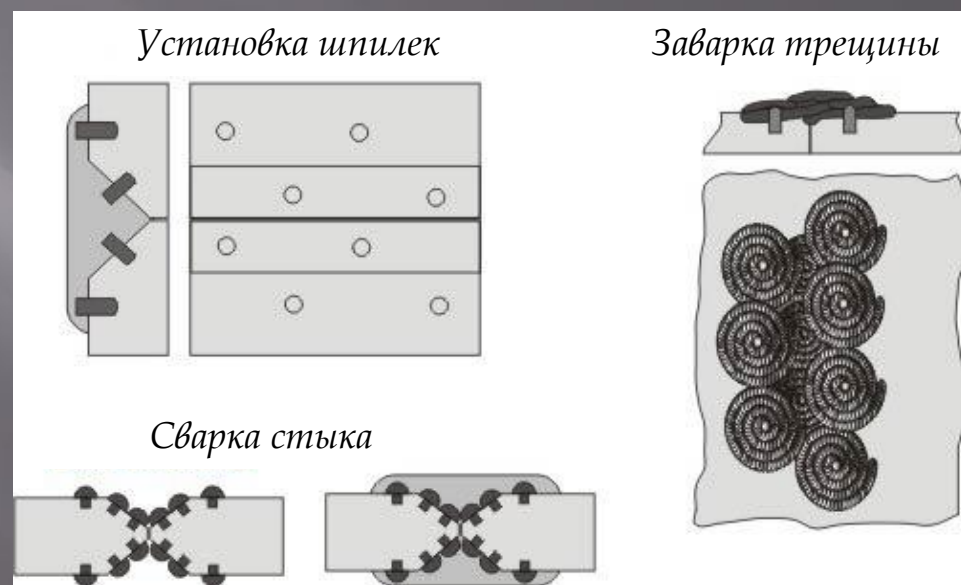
Использование шпилек при сварке чугуна
